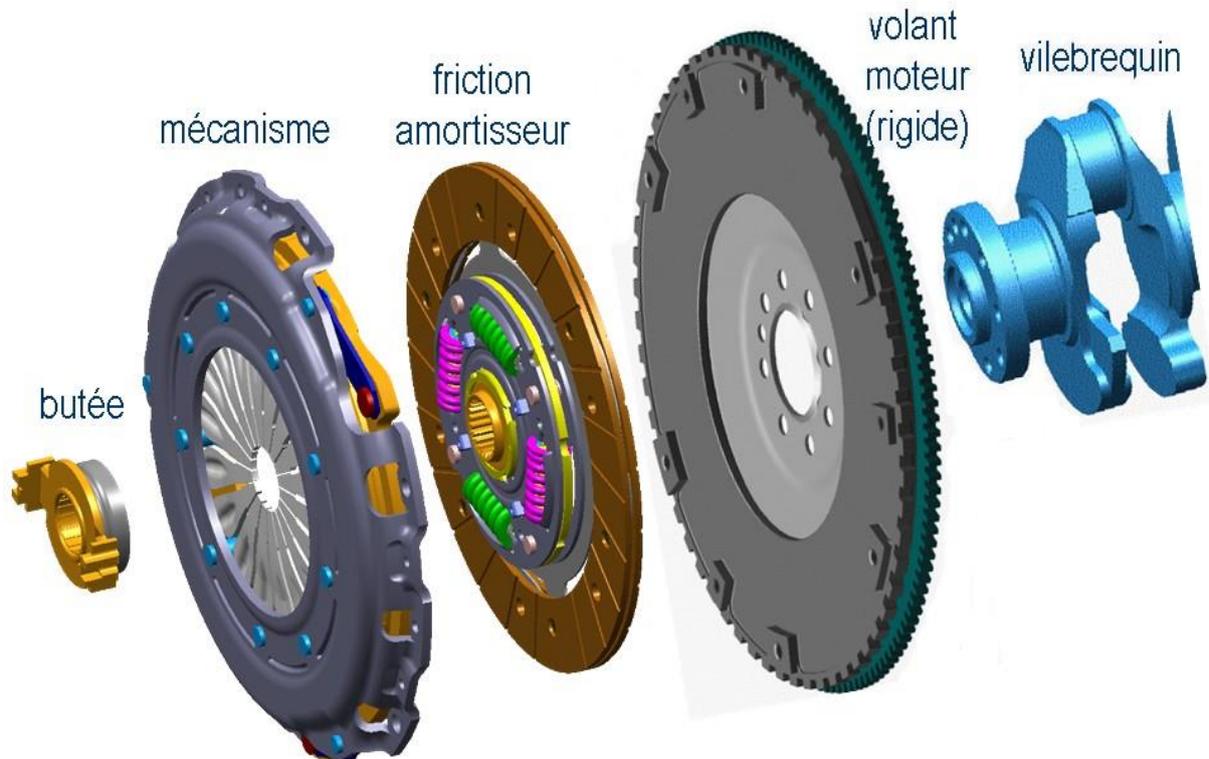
Vue d'ensemble du kit d'embrayage [29]
